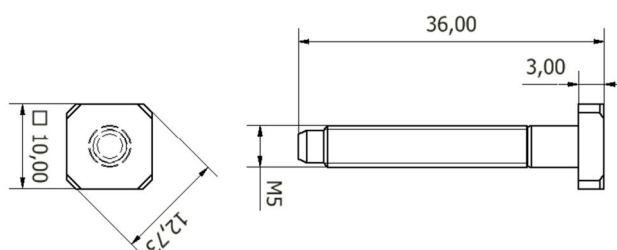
Dimensões do parafuso [imagem gerada no software de CAD utilizado]
